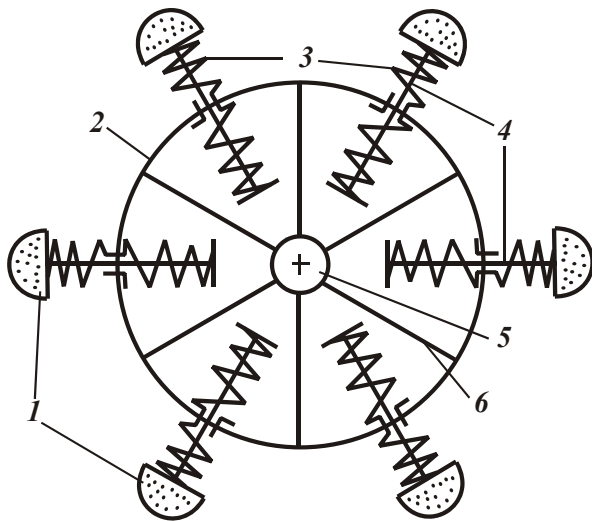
Шлифовальный инструмент для обработки внутренних поверхностей: 1 – шлифовальный брусок; 2 – корпус цилиндрический; 3 – пружина; 4 – штырь; 5 – вал; 6 – ребра жесткости.
